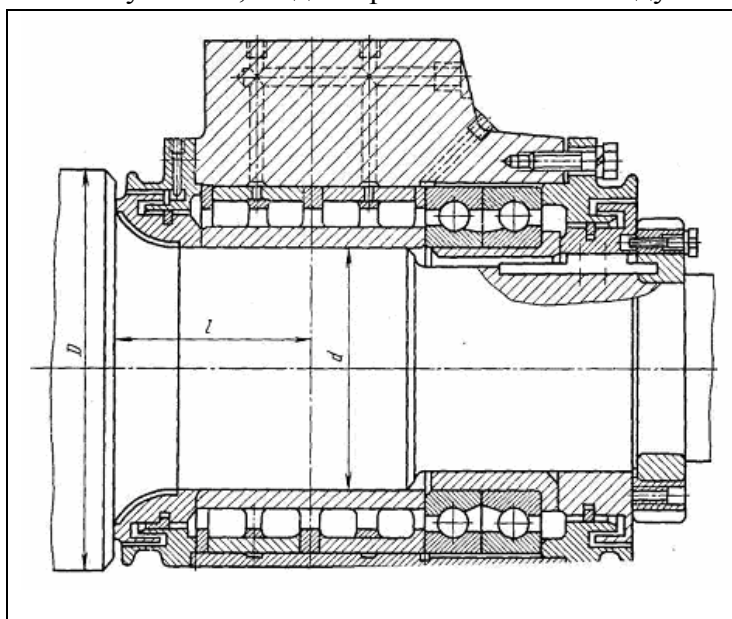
Четырехрядный подшипник с цилиндрическими роликами
